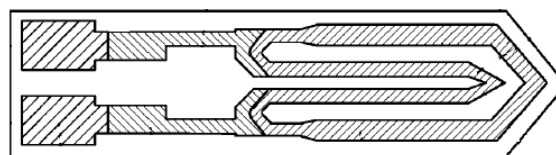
Планарный нагревательный элемент с резисторной структурой с положительным ТКС
